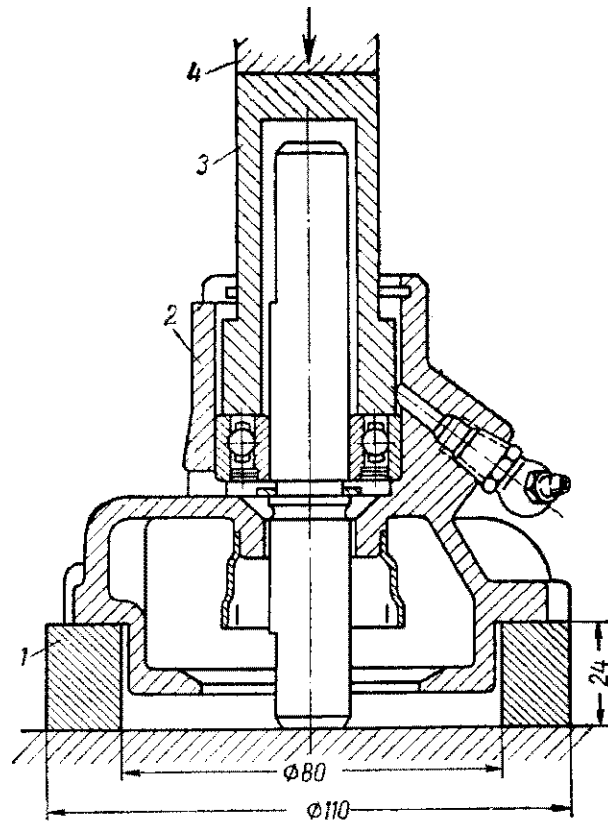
Запрессовка валика вместе с подшипниками в корпус насоса:
